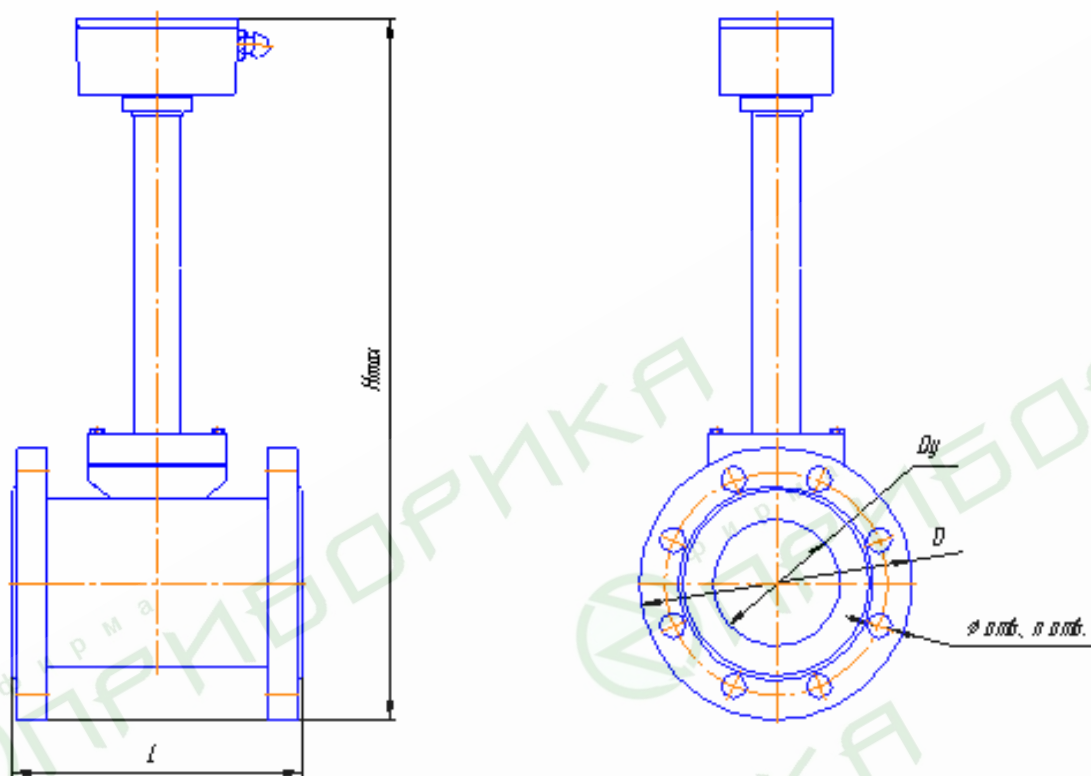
Габаритные, установочные, присоединительные размеры и масса преобразователь расхода - фланцевое соединение.
